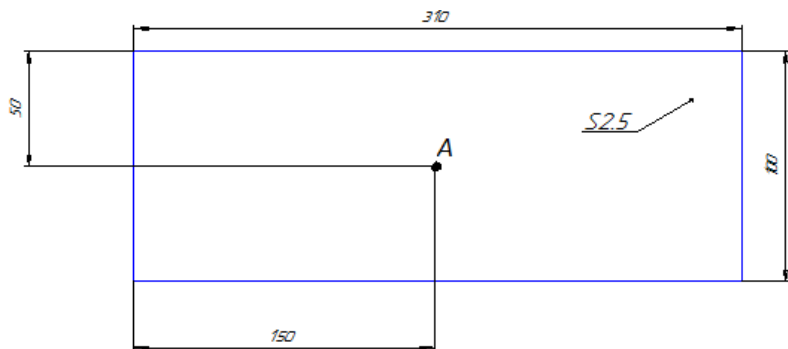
Общий вид образца и положение контрольной точки: А – точка для измерения магнитошумового параметра (МП)
